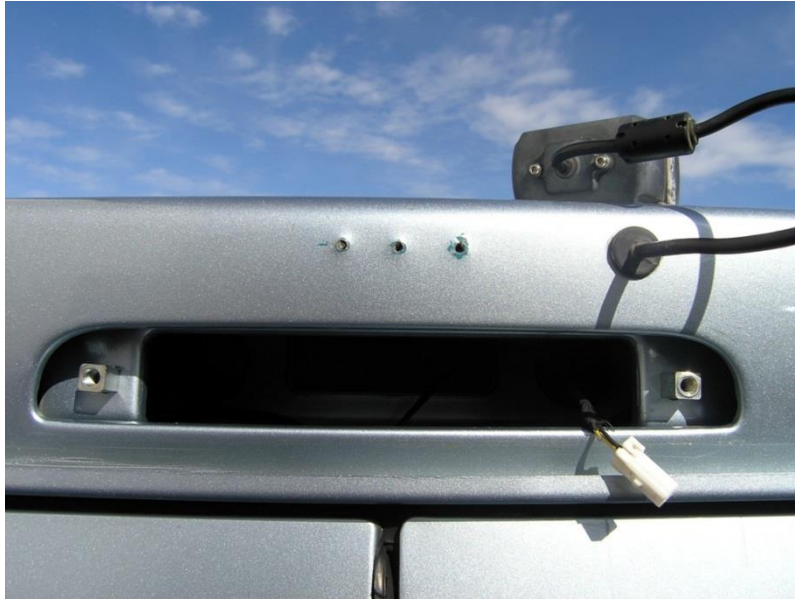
Entfernte 3. Bremsleuchte und Rückfahrkamera
